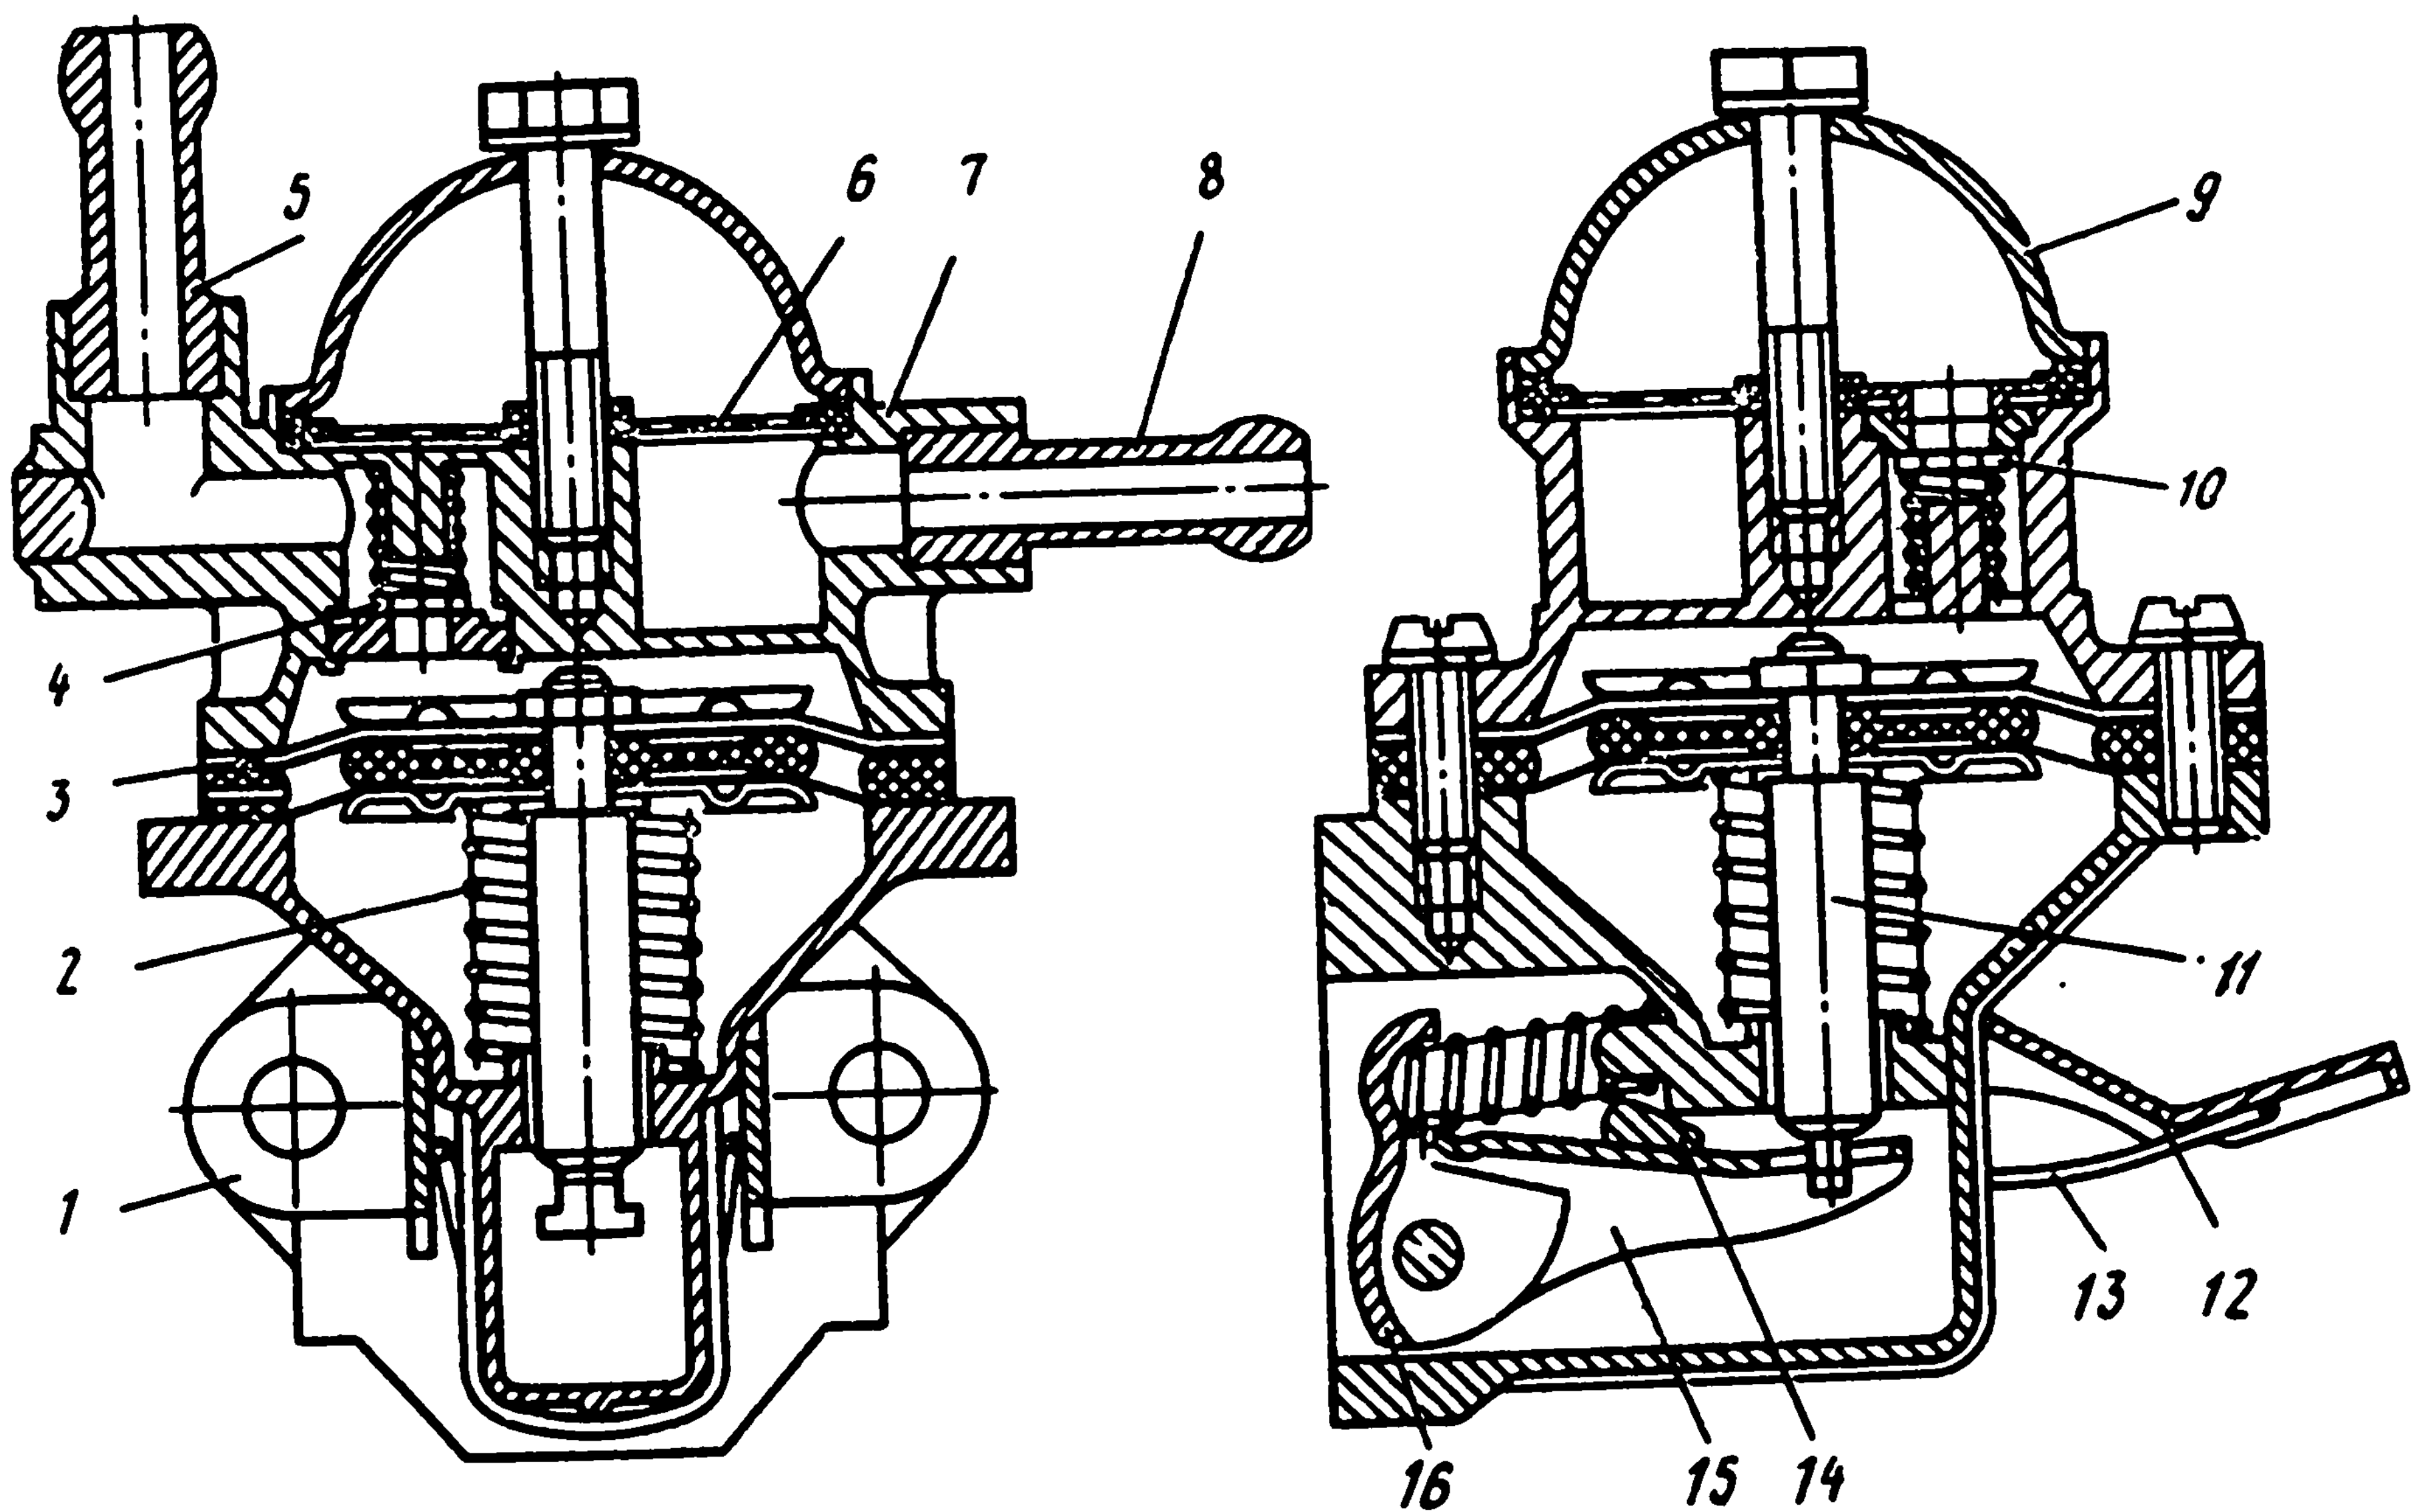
Топливный насос автомобиля ВАЗ-2121
